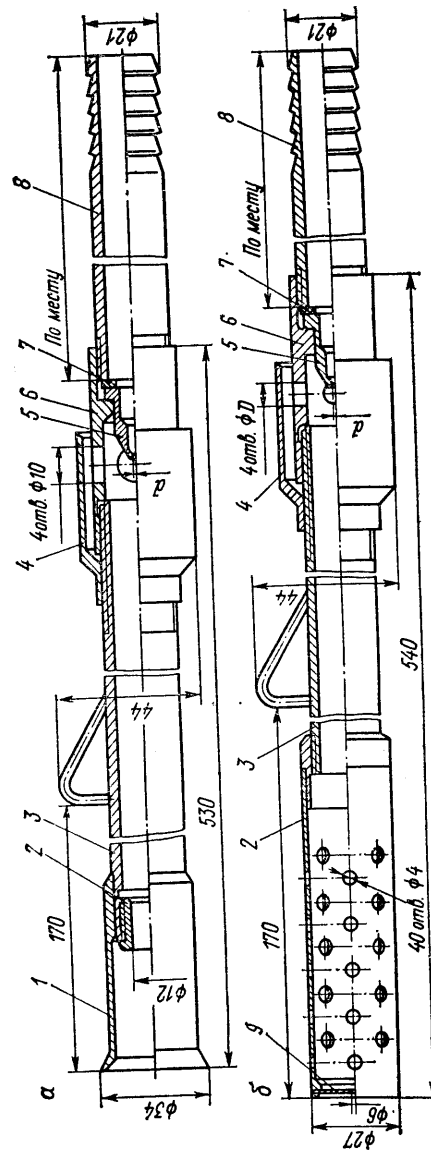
Запальник инжекционный для топок с разрежением. а — однофакельный; б — многофакельный; 1 — защитный кожух; 2 — огневой насадок; 3 — смеситель; 4 — воздушная обойма; 5 — сопло; 6 — сопло; 7 — инжектор; 8 — прокладка; 9 — удлинитель; 9 — горцевая пластина с отверстием.
